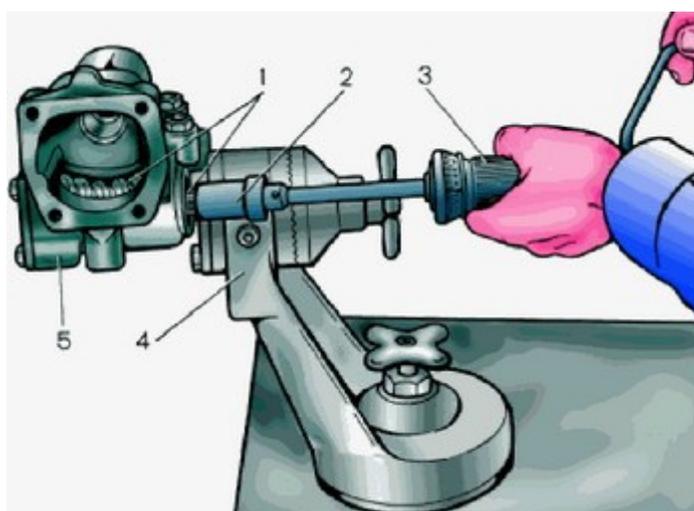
Контроль момента трения червяка динамометром: 1 - червяк; 2 - головка А.95697/5; 3 - динамометр 02.7812.9501; 4 - кронштейн станда для ремонта картера рулевого механизма; 5 - картер рулевого механизма
